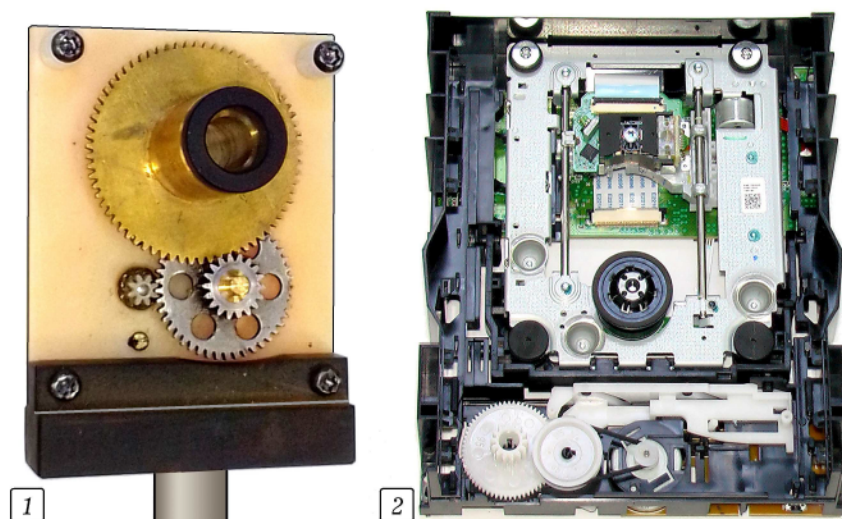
Для электромеханического блока можно использовать: 1 — самодельный редуктор из подходящих по параметрам зубчатых колес; 2 — электродвигатель и редуктор от привода устаревших оптических *DVD RW* дисков компьютера
